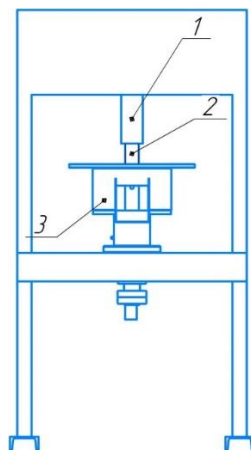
1 – шток пресса, 2 – ведомый вал, 3 – прессующий узел.
